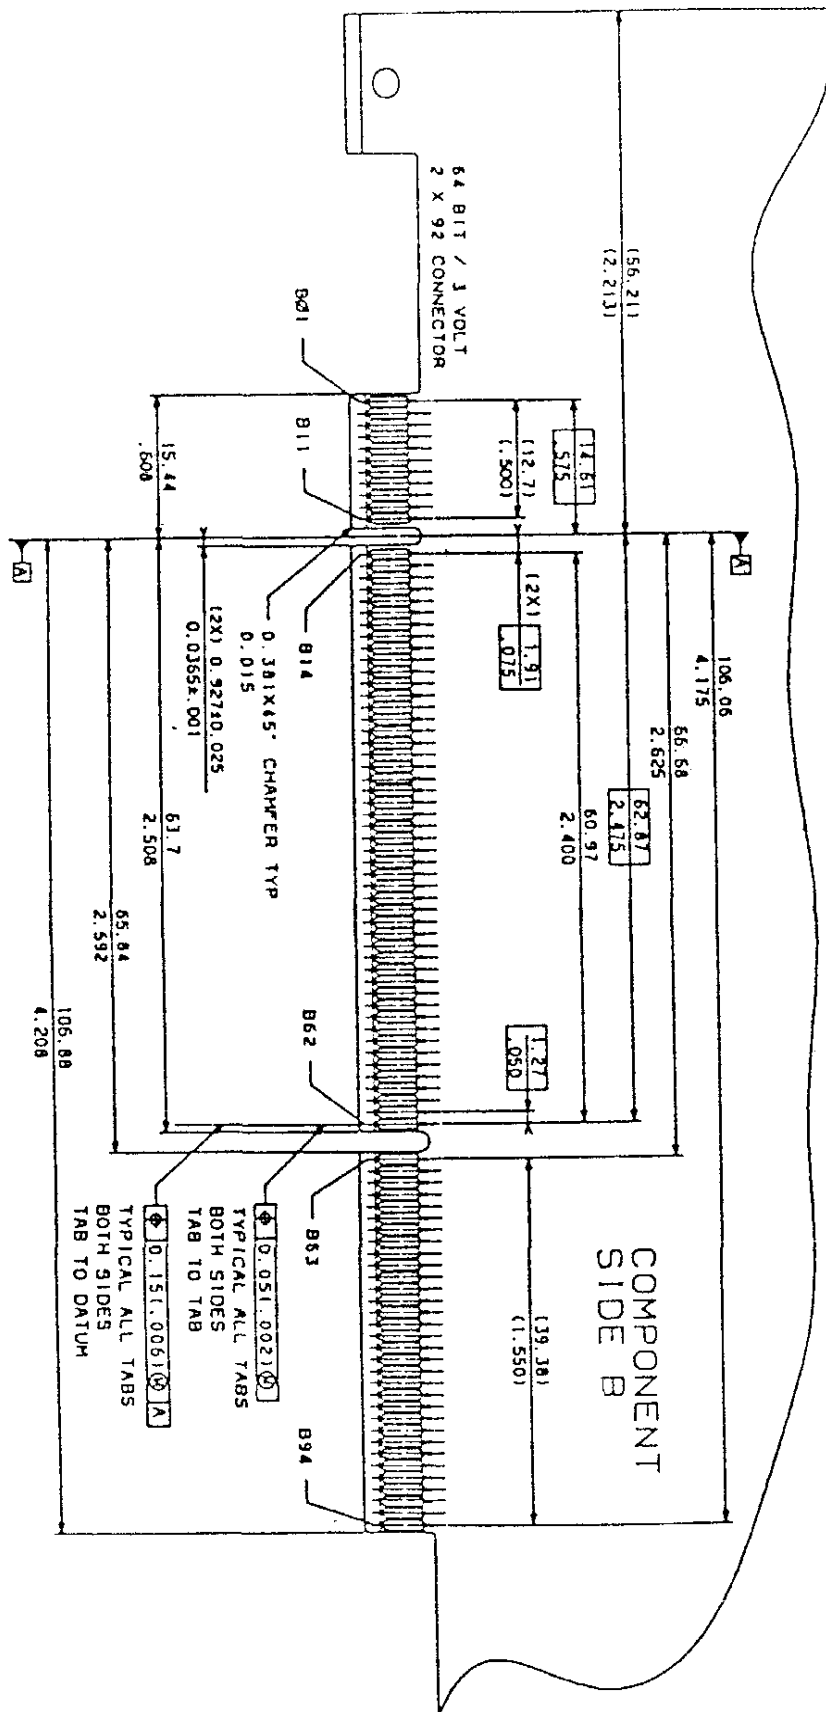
Размеры 3.3V/64-битового соединительного устройства для плат и допуски
